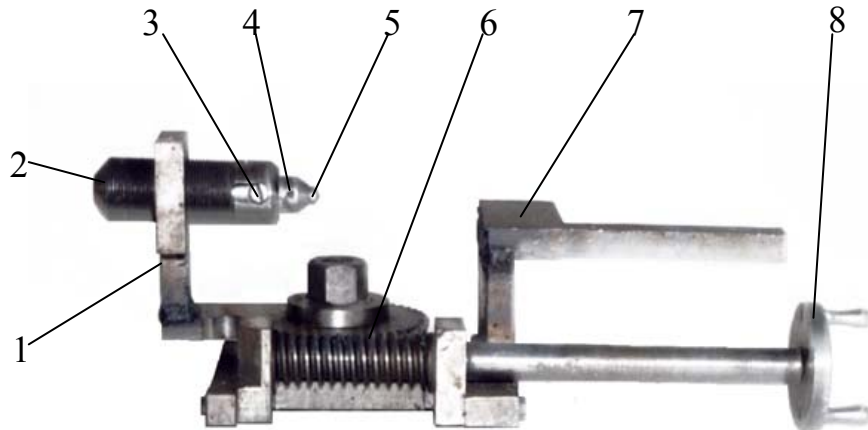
Пристрій для вигладжування пальців рульового керування вантажних автомобілів: 1 – кронштейн вигладжувача; 2 – корпус; 3 – показник сили вигладжування; 4 – повзун; 5 – індентор; 6 – черв'ячна пара; 7 – кронштейн для закріплення пристрою в супорті токарного верстата; 8 – рукоятка управління подачею індентора
